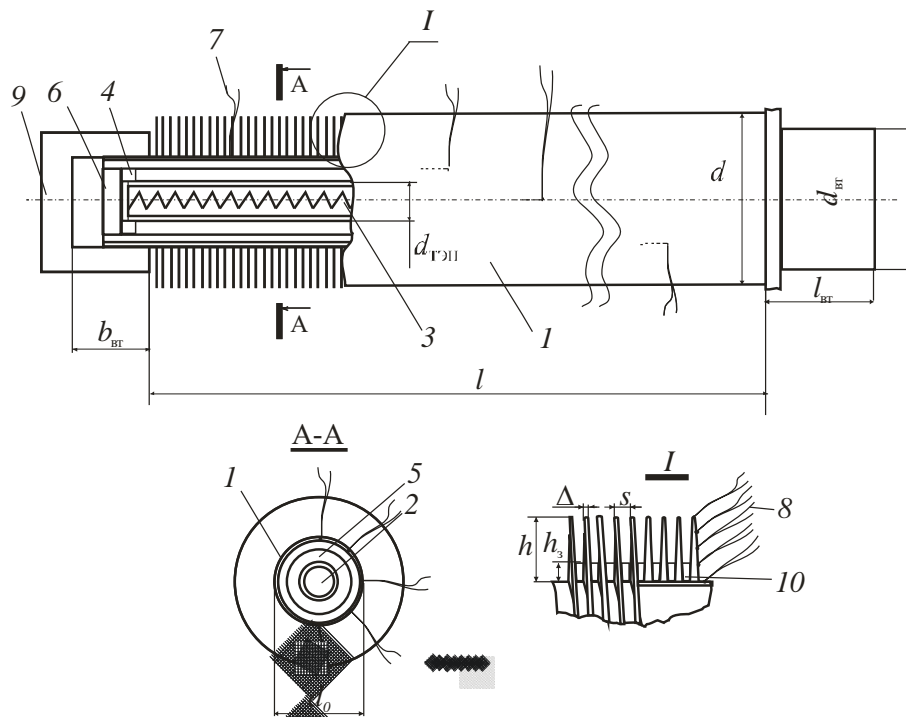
Общий вид калориметрической трубы: 1 – биметаллическая ребристая труба; 2 – трубчатый электронагреватель (ТЭН); 3 – спираль ТЭНа; 4 – центровочное кольцо; 5 – кварцевый песок; 6 – высокотемпературная силиконовая замазка; 7 – медь-константановые термопары у основания ребер; 8 – медь-константановые термопары по высоте ребра; 9 – фторопластовая втулка; 10 – льняной шнур
